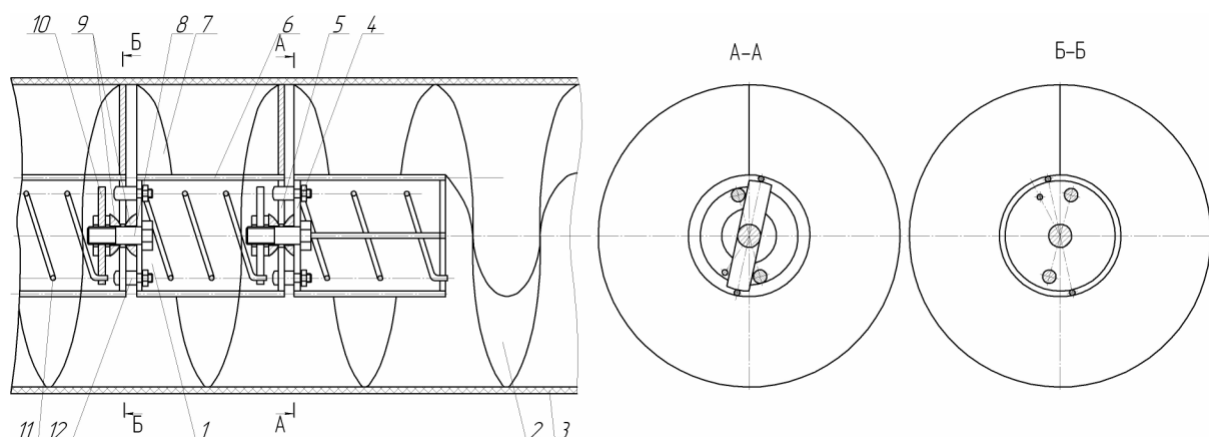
Пружний гнучкий гвинтовий робочий орган
